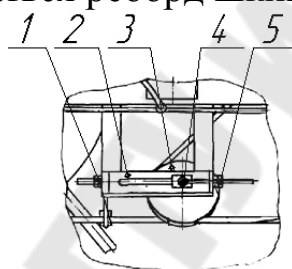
Схема регулировки натяжения ремня: 1, 5 – гайки; 2 – рамка; 3 – шкив натяжной; 4 – гайка
